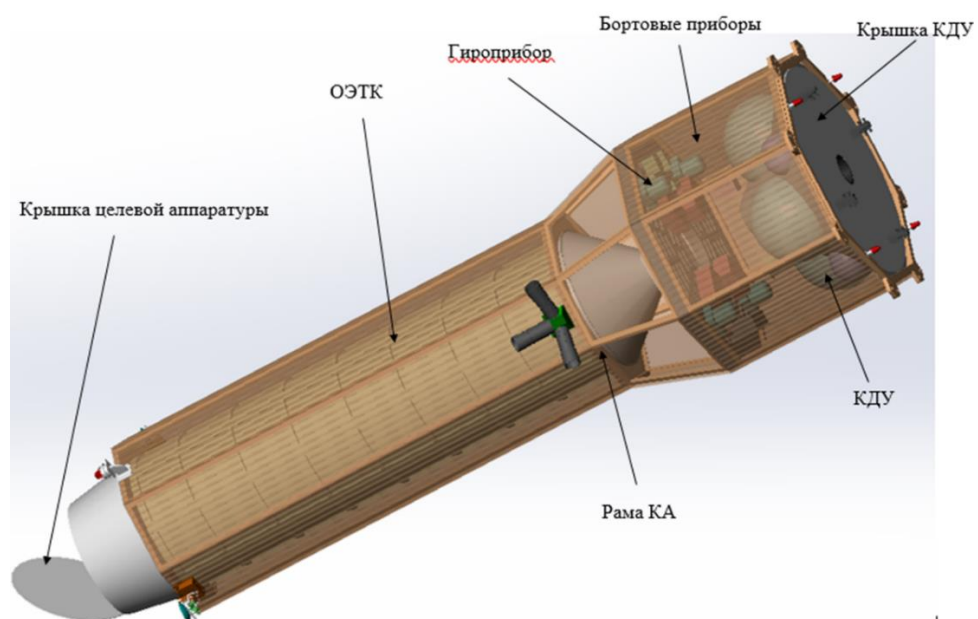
Схема формирования сборки корпуса КА и внутренних элементов
